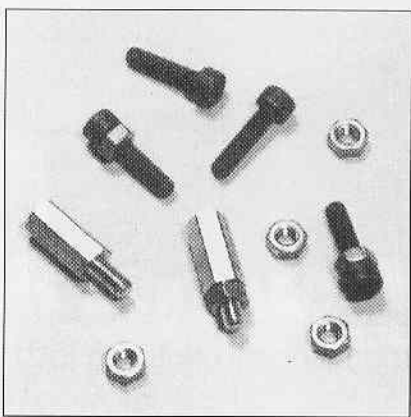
Bei vier Inbusschrauben und zwei Abstandsbolzen wird die Gewindel nge durch eine Mutter verk rzt.
